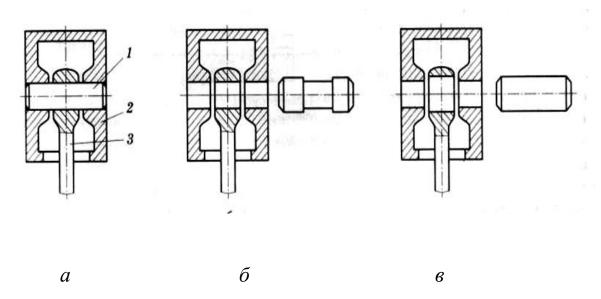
Соединение поршневого пальца с поршнем и шатуном двигателя автомобиля;
